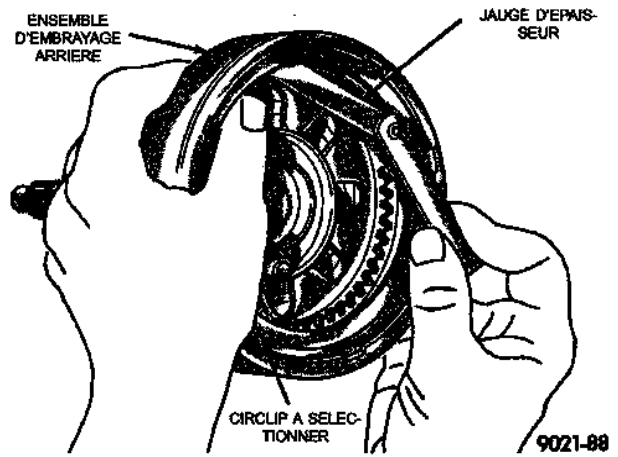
Mesure du jeu de plateau d'embrayage arrière
